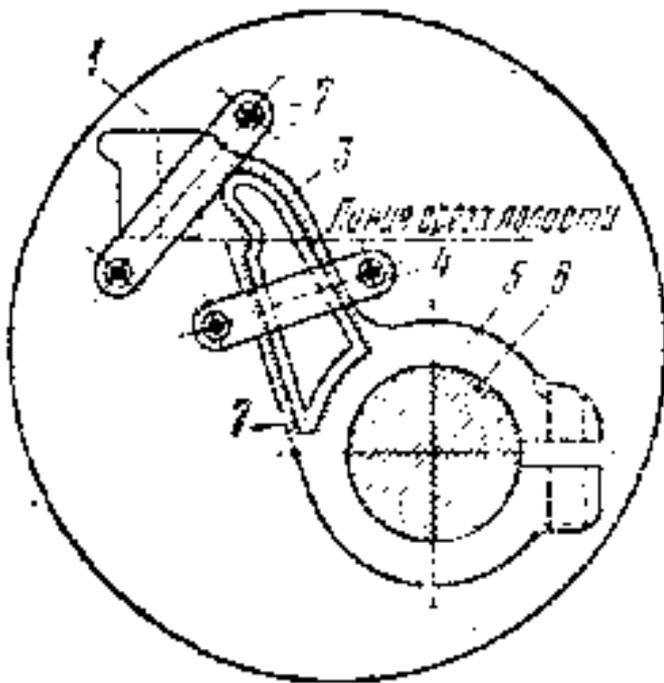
Кондуктор для ремонта лопасти сваркой.
